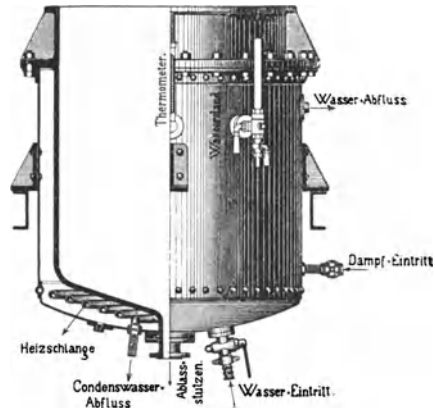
Kessel mit Heizschlange für Wasserbad usw. mit Einrichtung zum Kühlen
